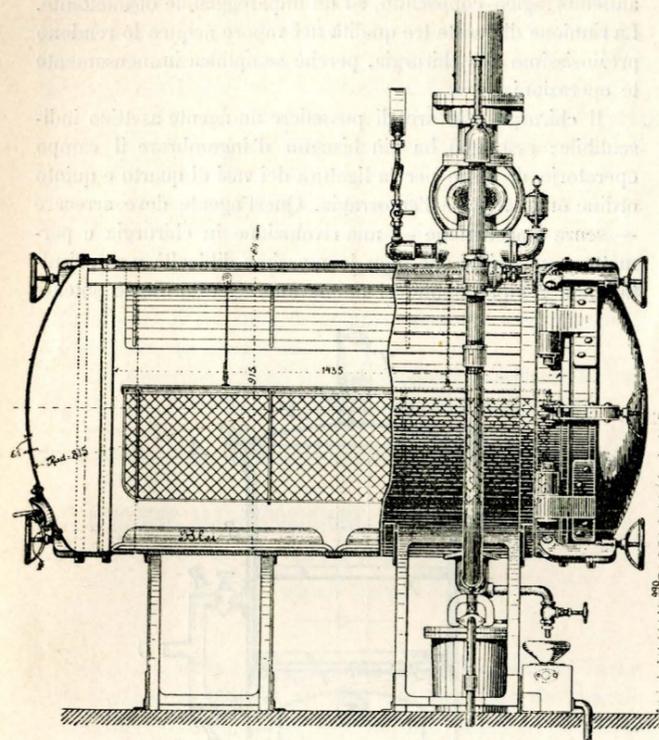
Sezione longitudinale e prospetto di fianco.
